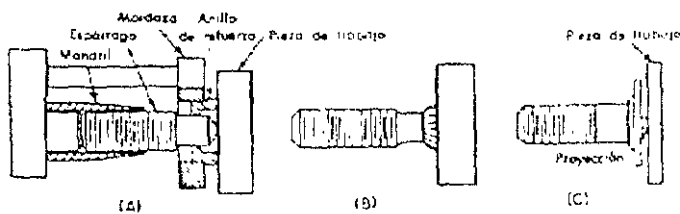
Procedimiento para soldadura de espárragos. A) Arreglo para soldadura con arco de espárragos. B) Un espárrago soldado con arco. C) Un espárrago para soldadura con descarga de capacitor.
